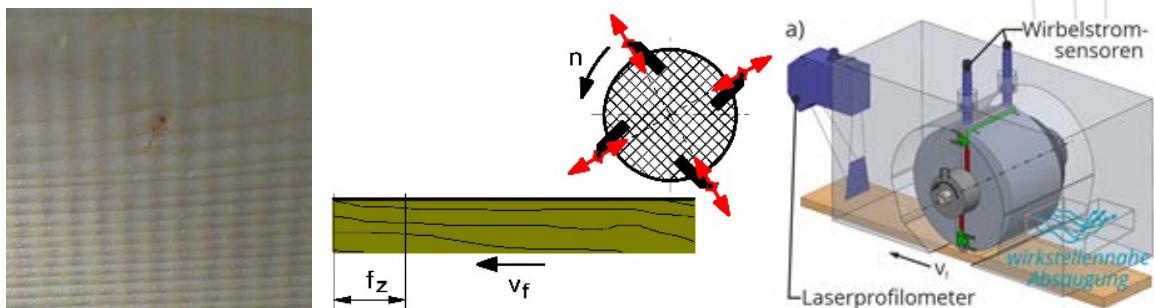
Foto der Messerschläge auf einem Holzwerkstück (links); Konzept der Messerschlagkompensation (Mitte); schematische Darstellung des aktiven Werkzeugs in einer Umfangsfräsmaschine (rechts)
